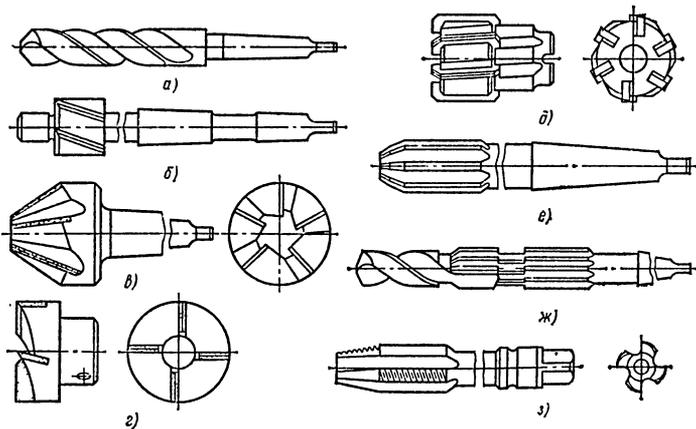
Инструменты для обработки отверстий на сверлильных станках
